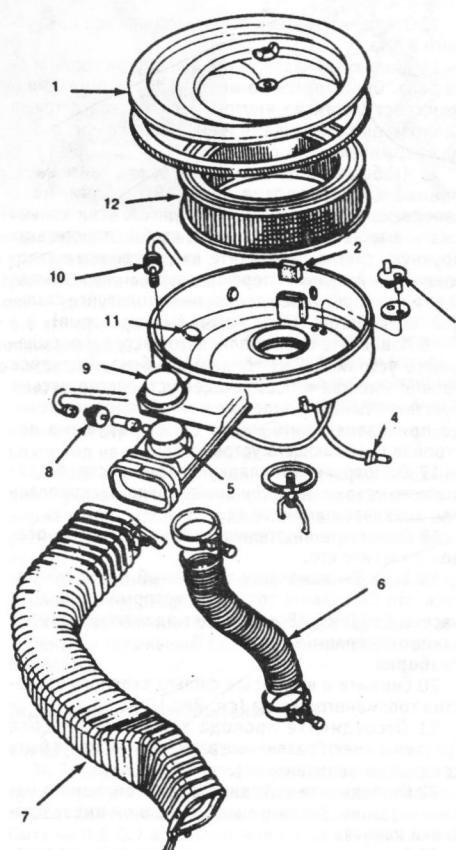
б Сборка воздухоочистителя — покомпонентное изображение (шестицилиндровый V-образный двигатель)
